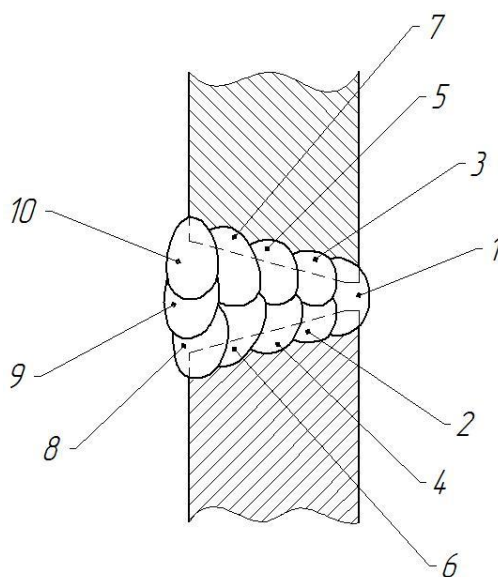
Сварное соединение и наложение валиков
